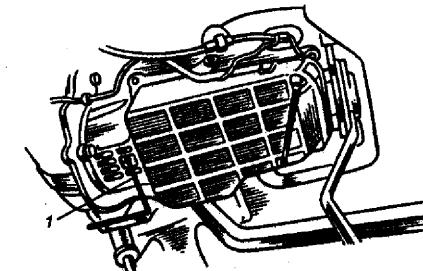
Установка торцевого ключа 1 для сливной пробки в окошко гидротрансформатора
